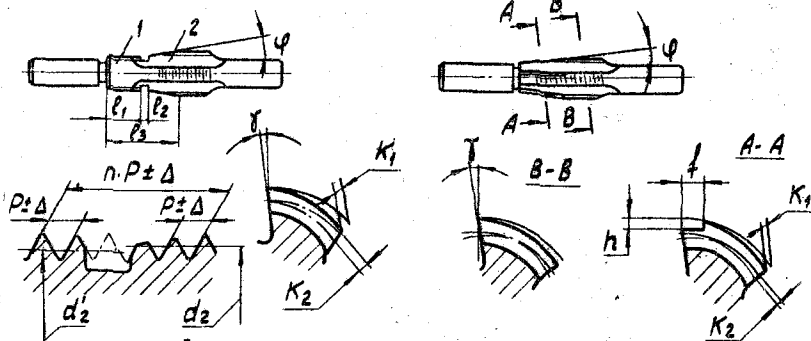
Метчик с передней резьбовой направляющей Рис. 6. Метчик с режуще-ведущими зубьями
